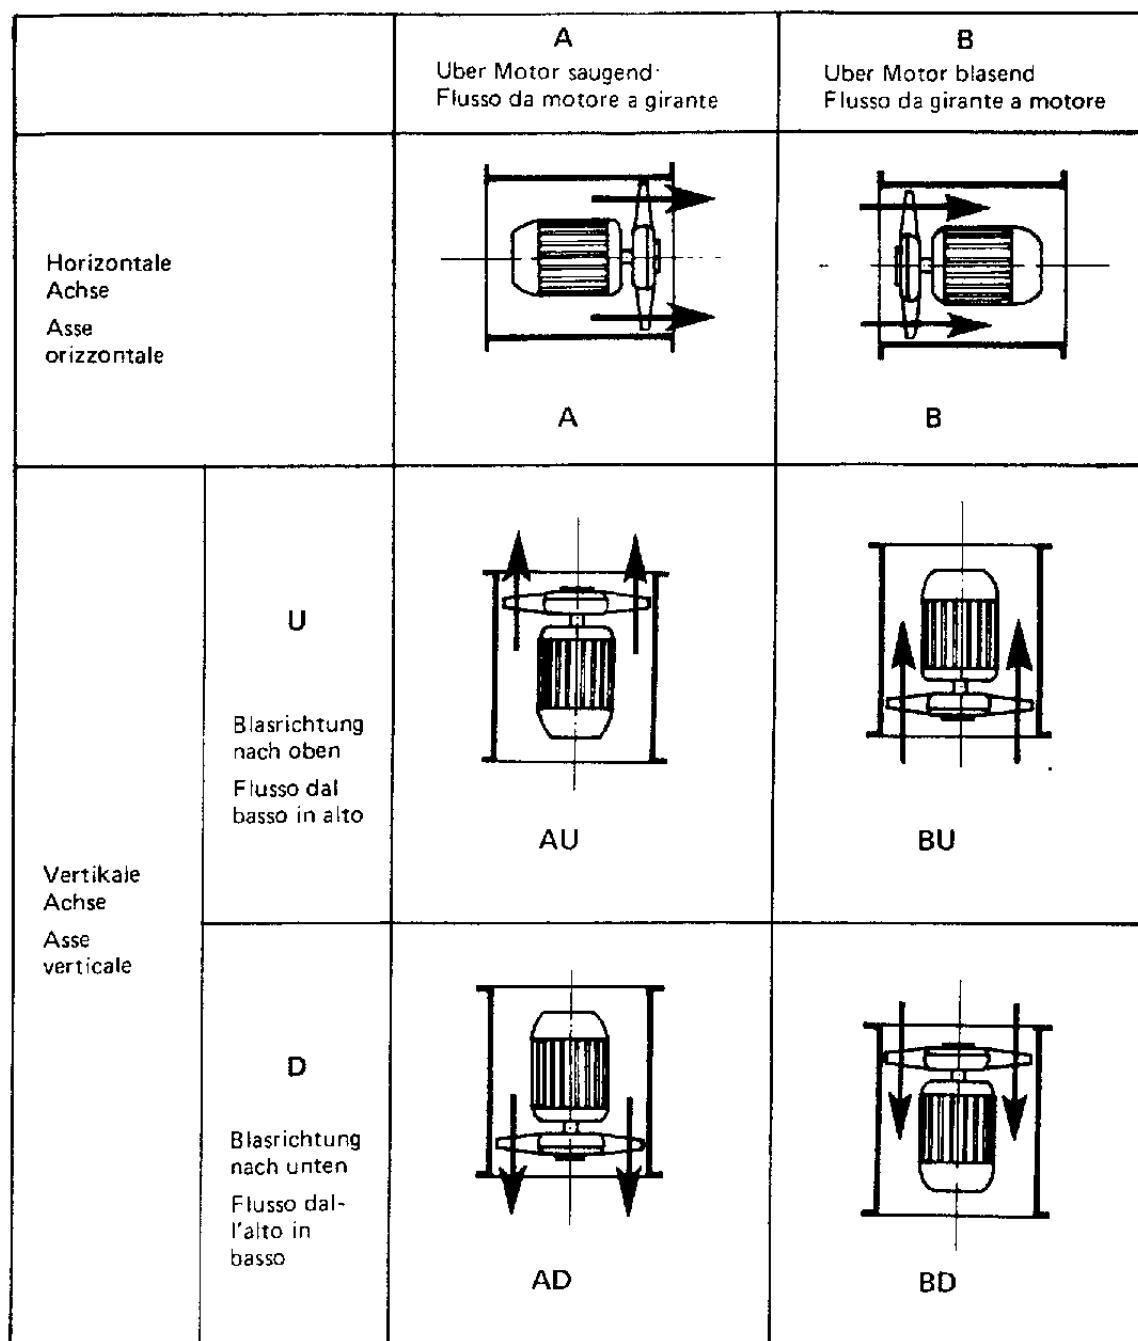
Bezeichnung der Lage des Motors in direkt angetriebenen Axial-, Halbaxial- und anderen Ventilatoren mit koaxialem Ein- und Austritt
